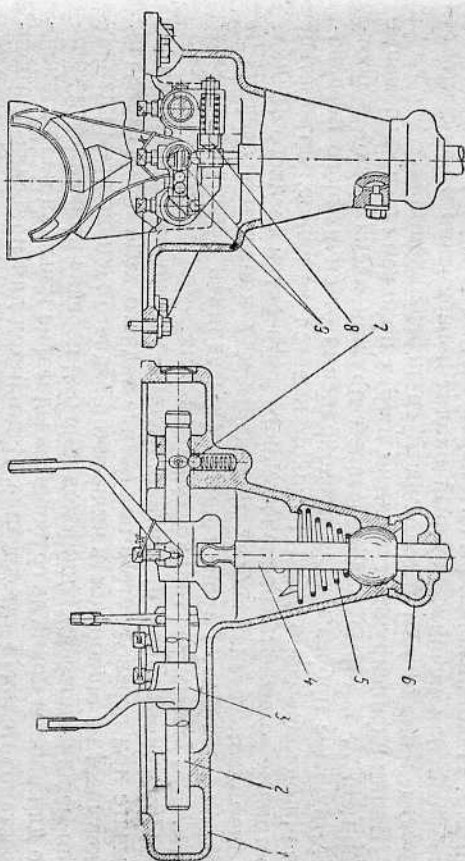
Механизм переключения шестерен коробки перемены передач: 1—крышка коробки передач; 2—валик; 3—вилка; 4—рычаг переключения; 5—пружина; 6—чехол; 7—шарик фиксатора; 8—пружинный упор; 9—замочное устройство
